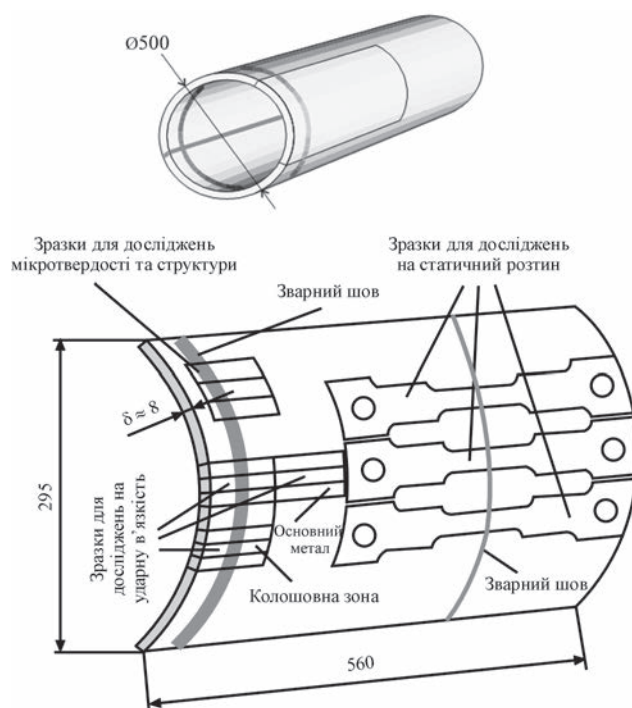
Схема виготовлення зразків з фрагменту контрольованої труби
